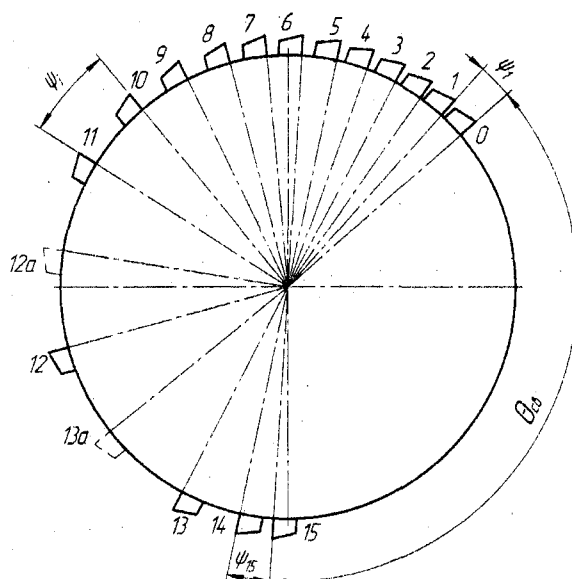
Схема расположения режущих элементов в резцовой головке для стабилизированного процесса обкатывающего зубопротягивания
